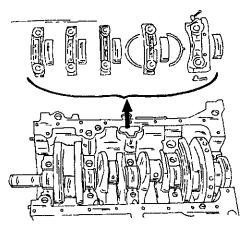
Сборка крышек коренных подшипников, вкладышей подшипников и разгонных шайб на двигателе типа XU (с или без рабочих гильз цивиндров).
